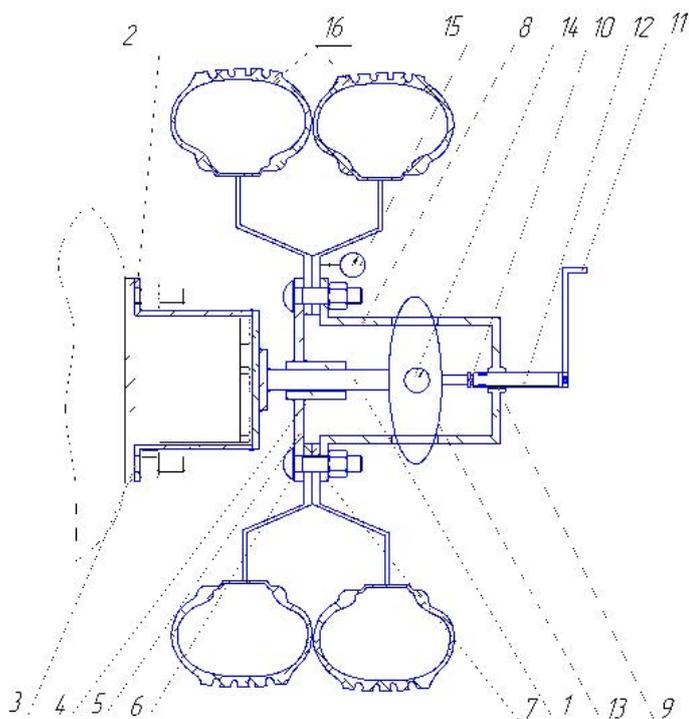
Стенд для определения бокового сцепления и боковой жесткости шин [11]:
